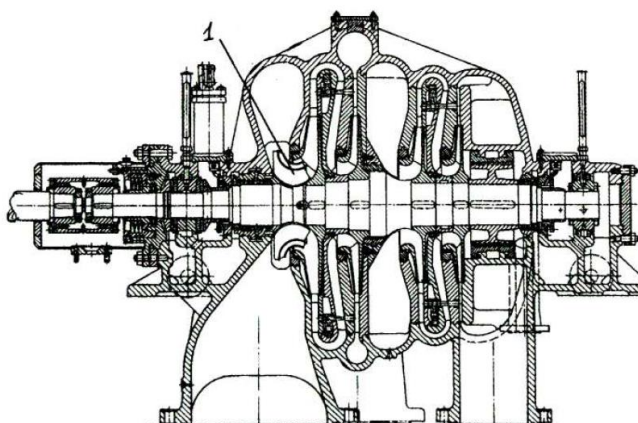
Холодильный центробежный компрессор: 1 – входной направляющий аппарат
